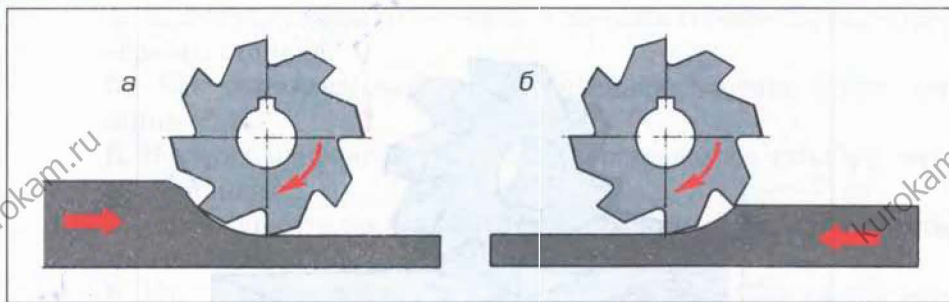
Виды фрезерования: а – встречное, б – попутное
